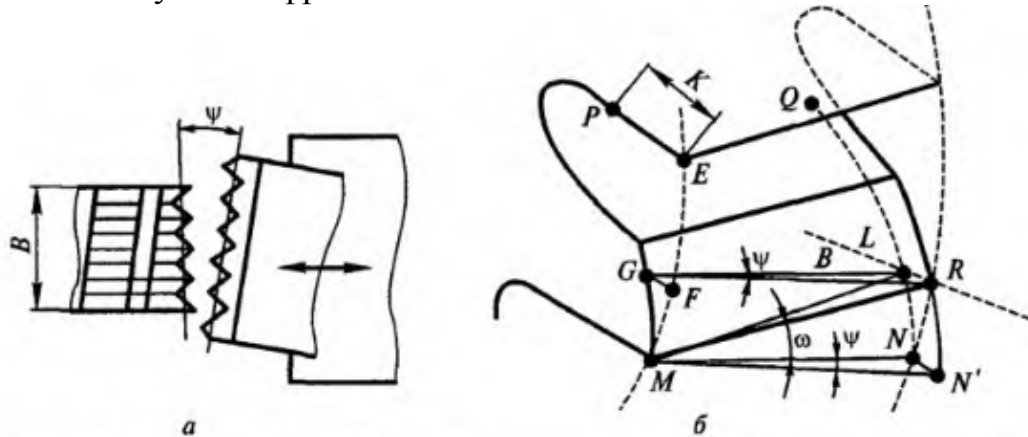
Затилування різьбової гребінчастої фрези з гвинтовими стружковими канавками: *a* – схема установки гребінки ; *б* – розрахована схема для визначення кута повороту гребінки
